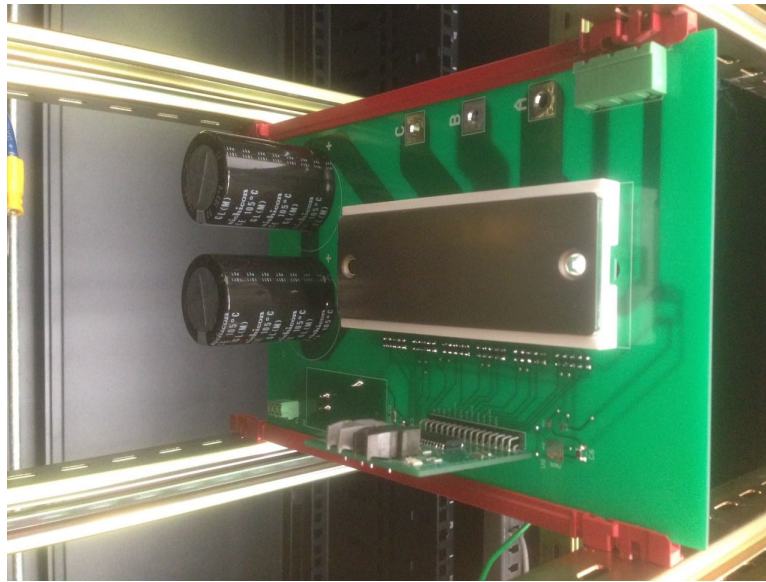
Vista lateral izquierda de montaje de celda en soporte construido sin disipador
